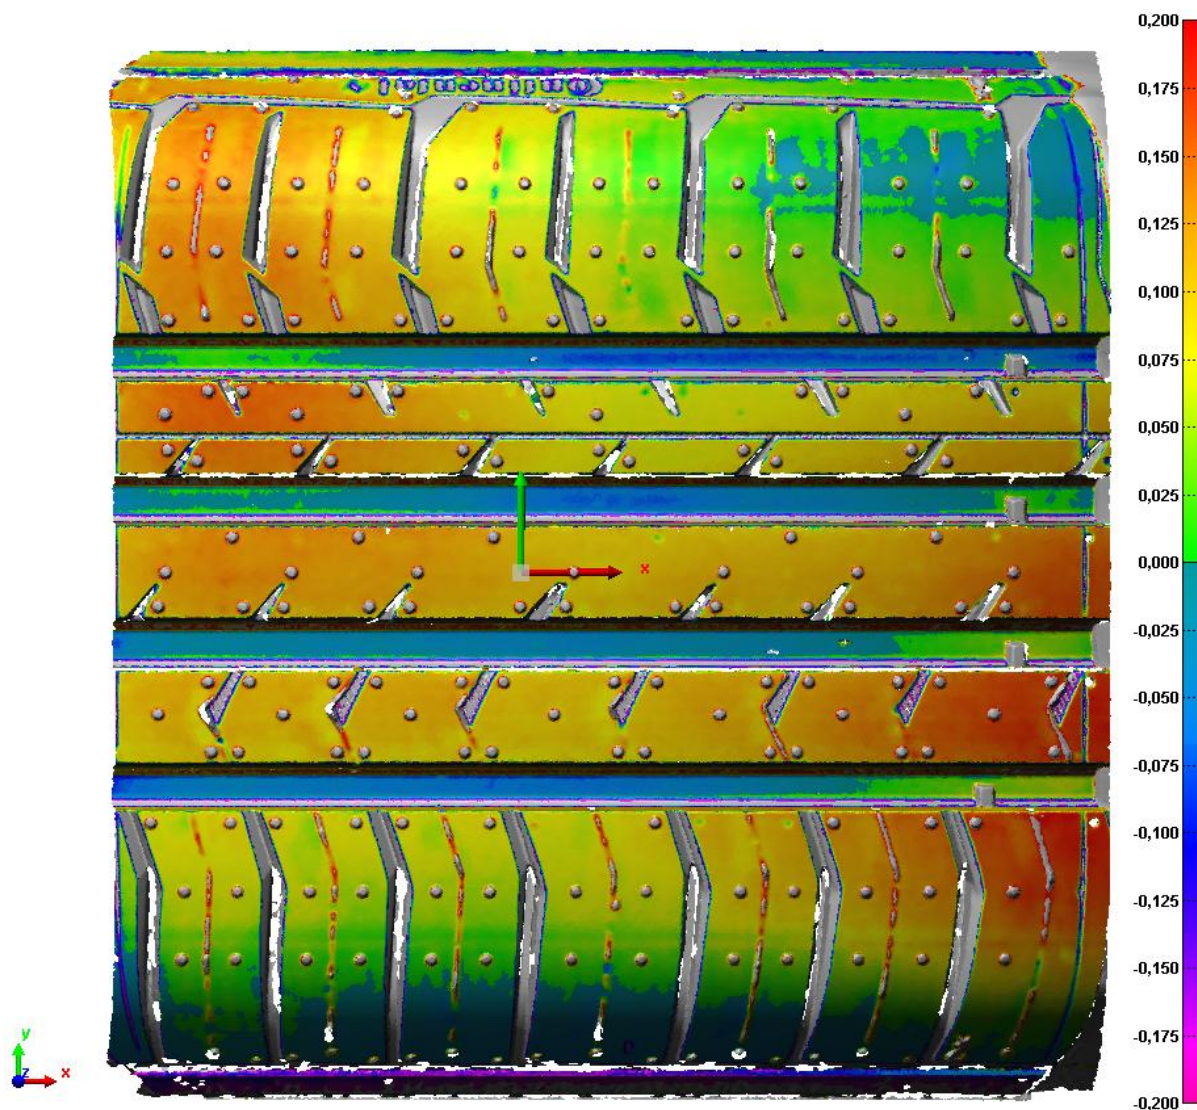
Sádrové jádro z materiálu Cenusil M820.
